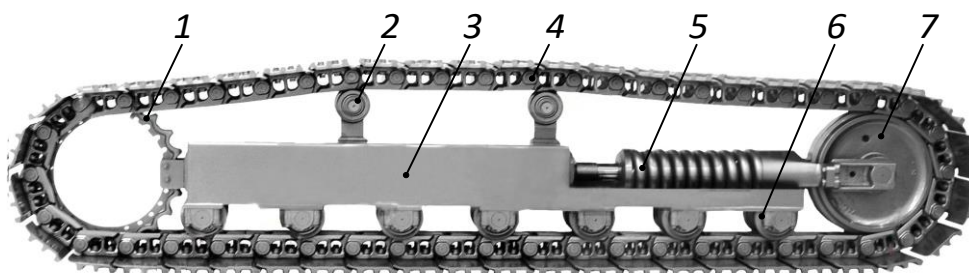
Ходова система гусеничного трактора: 1– ведуче колесо; 2 – підтримуючий ролик; 3 – рама; 4 – гусениця; 5 – пружина (амортизатор); 6 – опорний коток; 7 – напрямне колесо;
